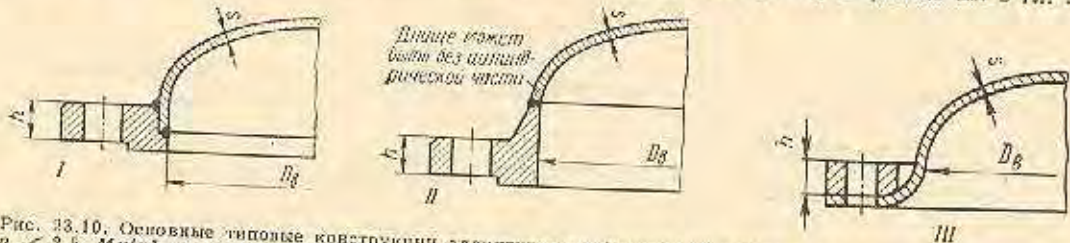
Основные типовые конструкции эллиптических фланцевых крышек: I — сварные стальные при $p_d \leq 2,5 \text{ Мн/м}^2$ и из цветных металлов при $p_d \leq 0,6 \text{ Мн/м}^2$; II — сварные стальные при $p_d > 2,5 \text{ Мн/м}^2$ и из цветных металлов при $p_d > 0,6 \text{ Мн/м}^2$; III — из меди с накладными фланцами при $p_d \leq 0,3 \text{ Мн/м}^2$
